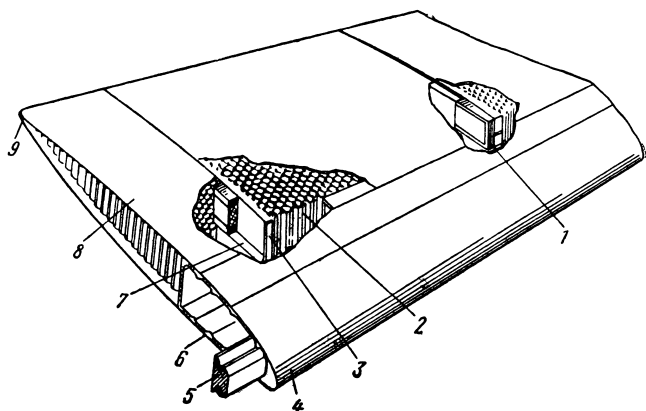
Типовой отсек лопасти несущего винта с прессованным дуралюминовым лонжероном:
